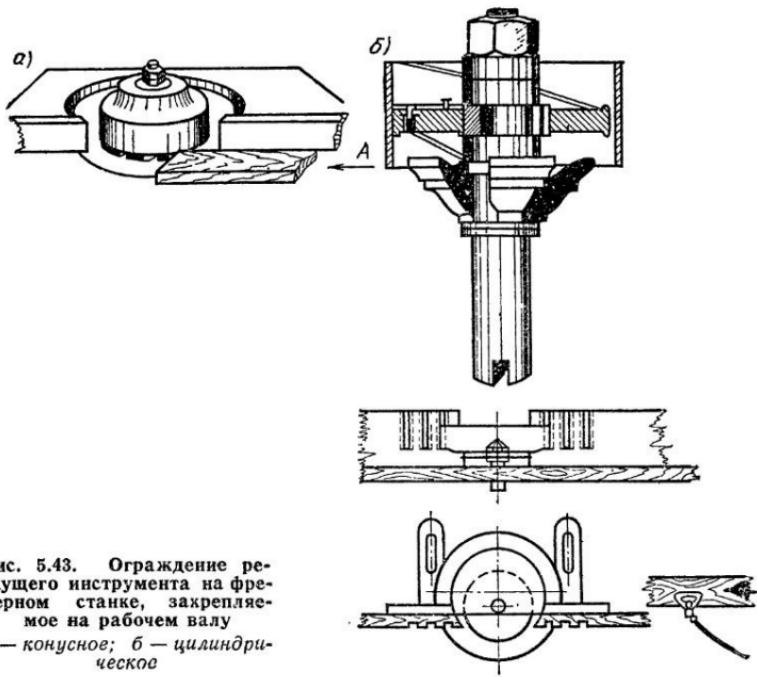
Ограждение режущего инструмента на фрезерном станке, закрепляемое на рабочем валу
